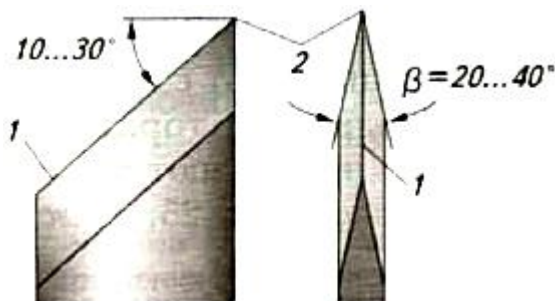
Лезвие косой токарной стамески: 1 — режущая кромка; 2 — вершина
